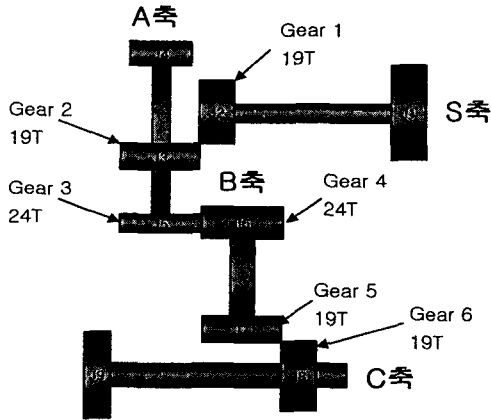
홀더의 Gear-and-Shaft 시스템의 개략도
